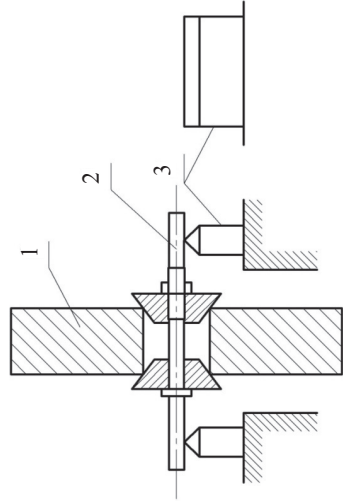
Схема балансировки колеса на призмах:
